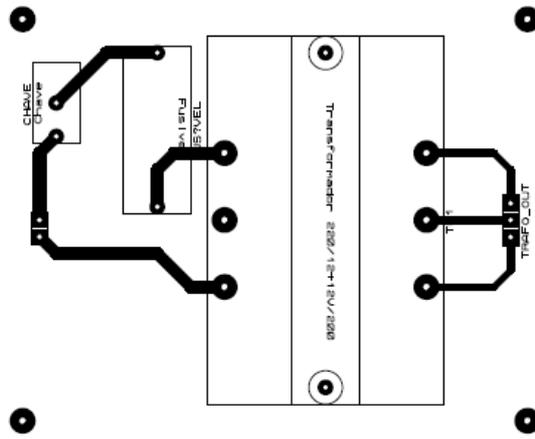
Desenho impresso para transferência para a placa auxiliar.
